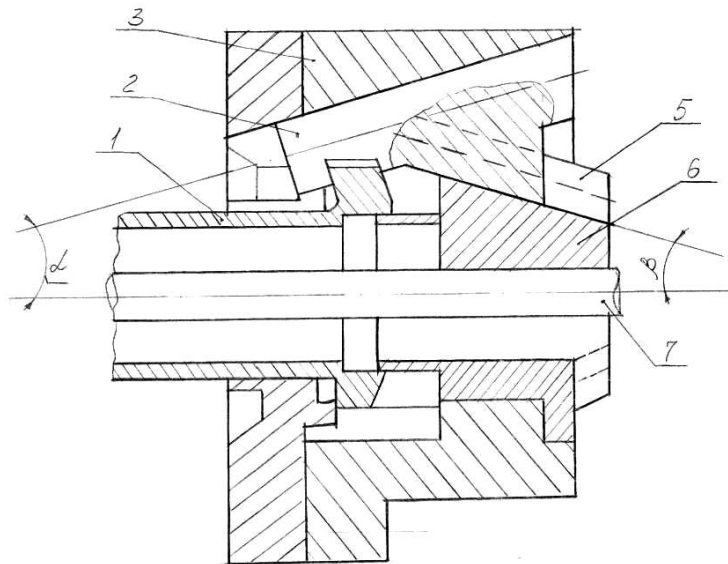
Широкодіапазонний клиноплунжерний патрон
